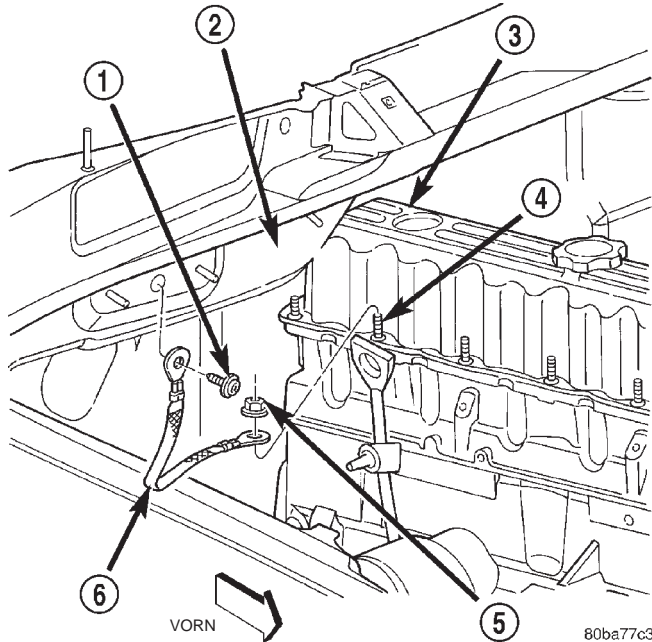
Masseband zwischen Motor und Karosserie aus- und einbauen—4.0L-Motor
